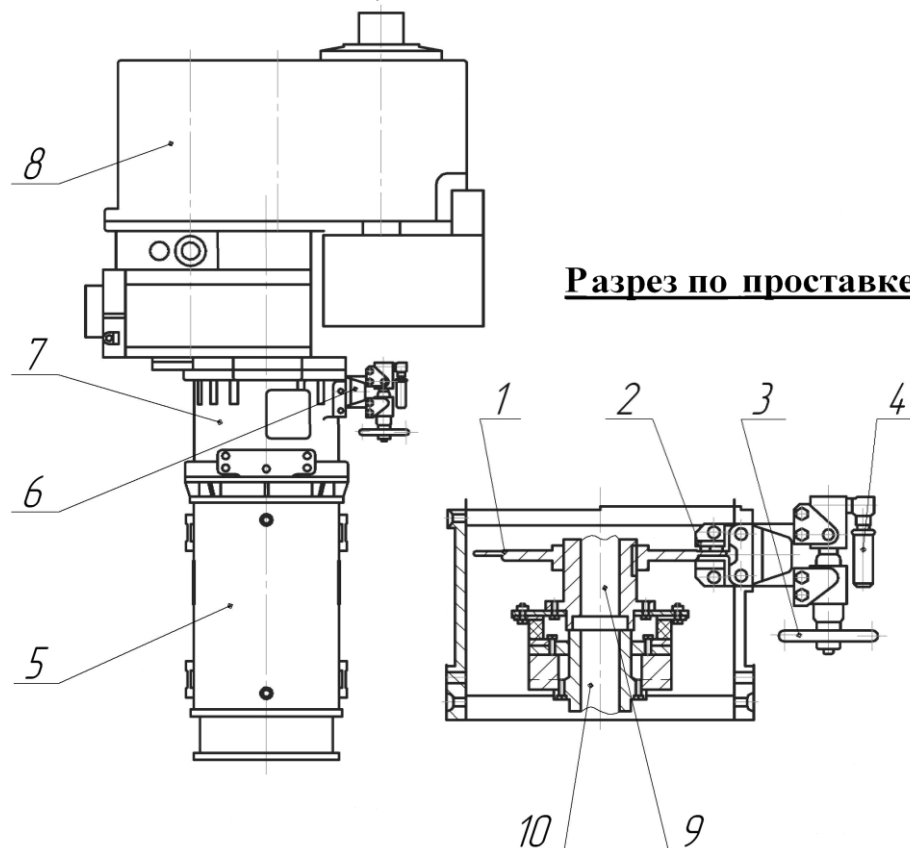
Привод с системой натяжения цепи ТНЦ:
